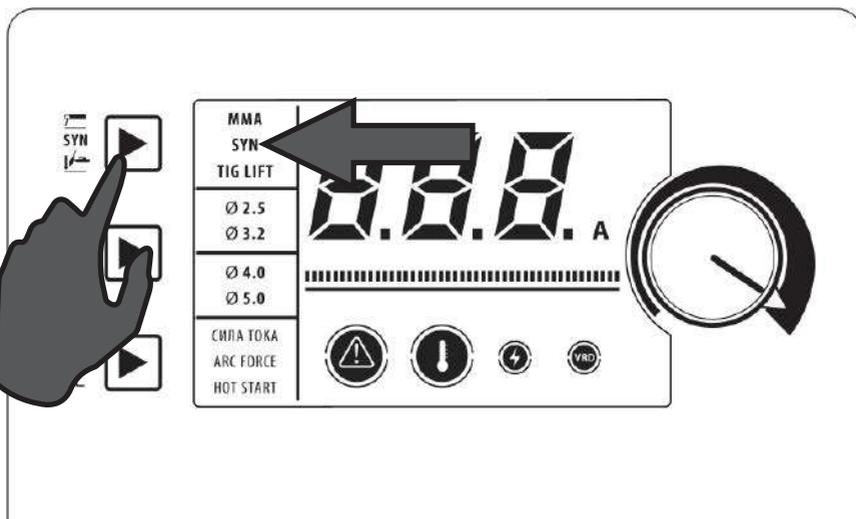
Выбор режима сварки SYN MMA DC.
